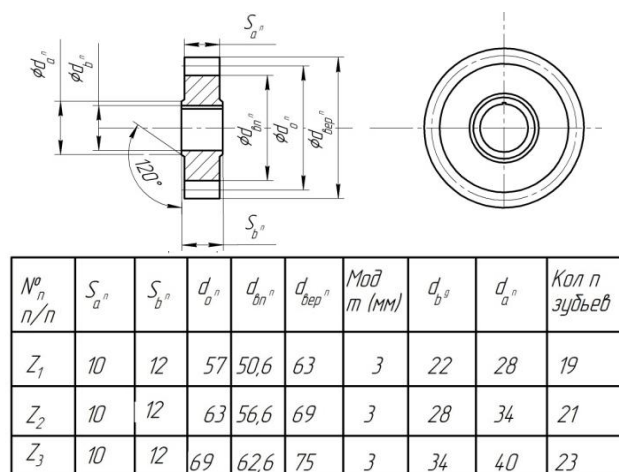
Эскиз групповой зубчатых колес, входящих в состав блок-вала колес.
